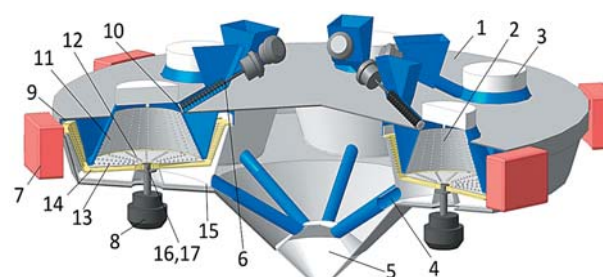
Установка с резонаторами в виде усечённого конуса-терки
